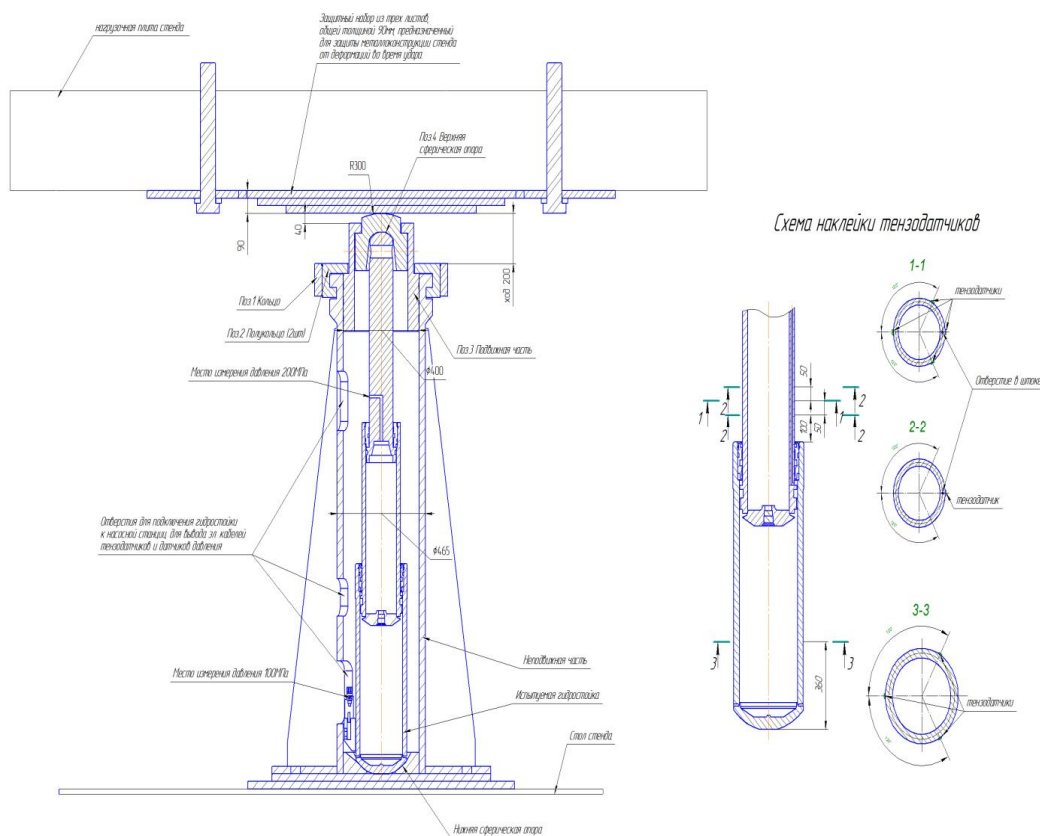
Схема динамических испытаний гидростойки на стенд К-10
